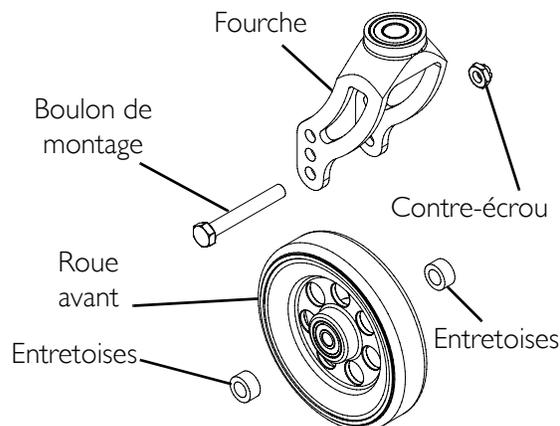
Enlever/Installer/Repositionner l'assemblage de la roue avant - Fourches standards
